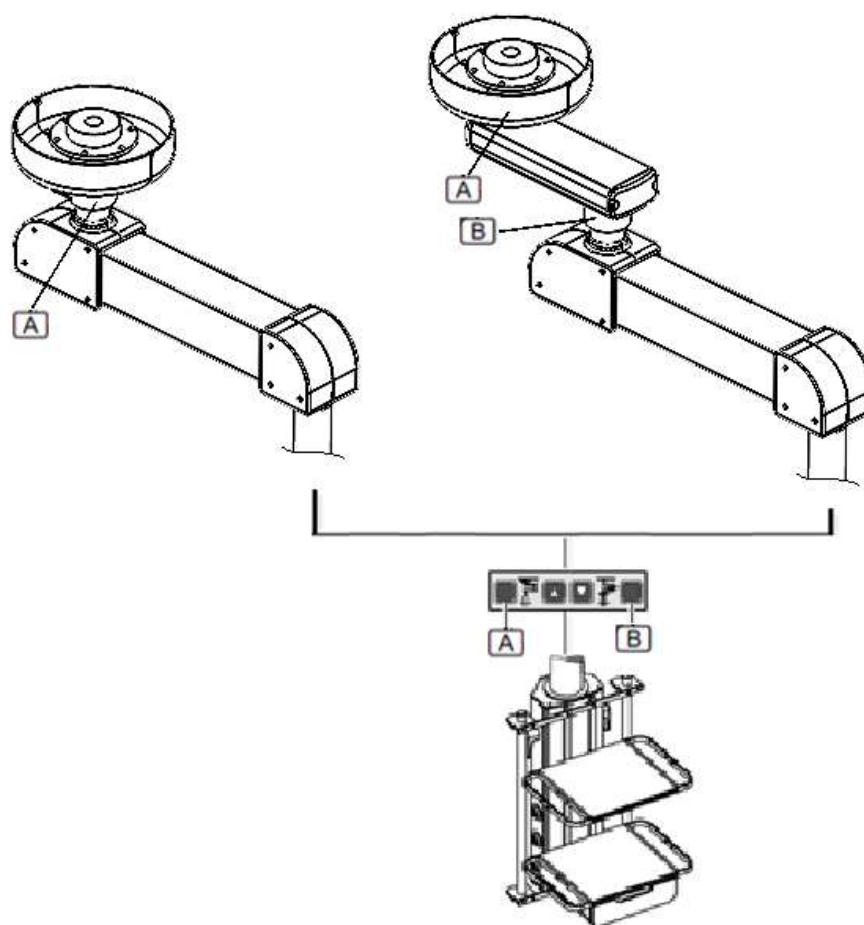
Positie van de remmen op de gemotoriseerde armen
